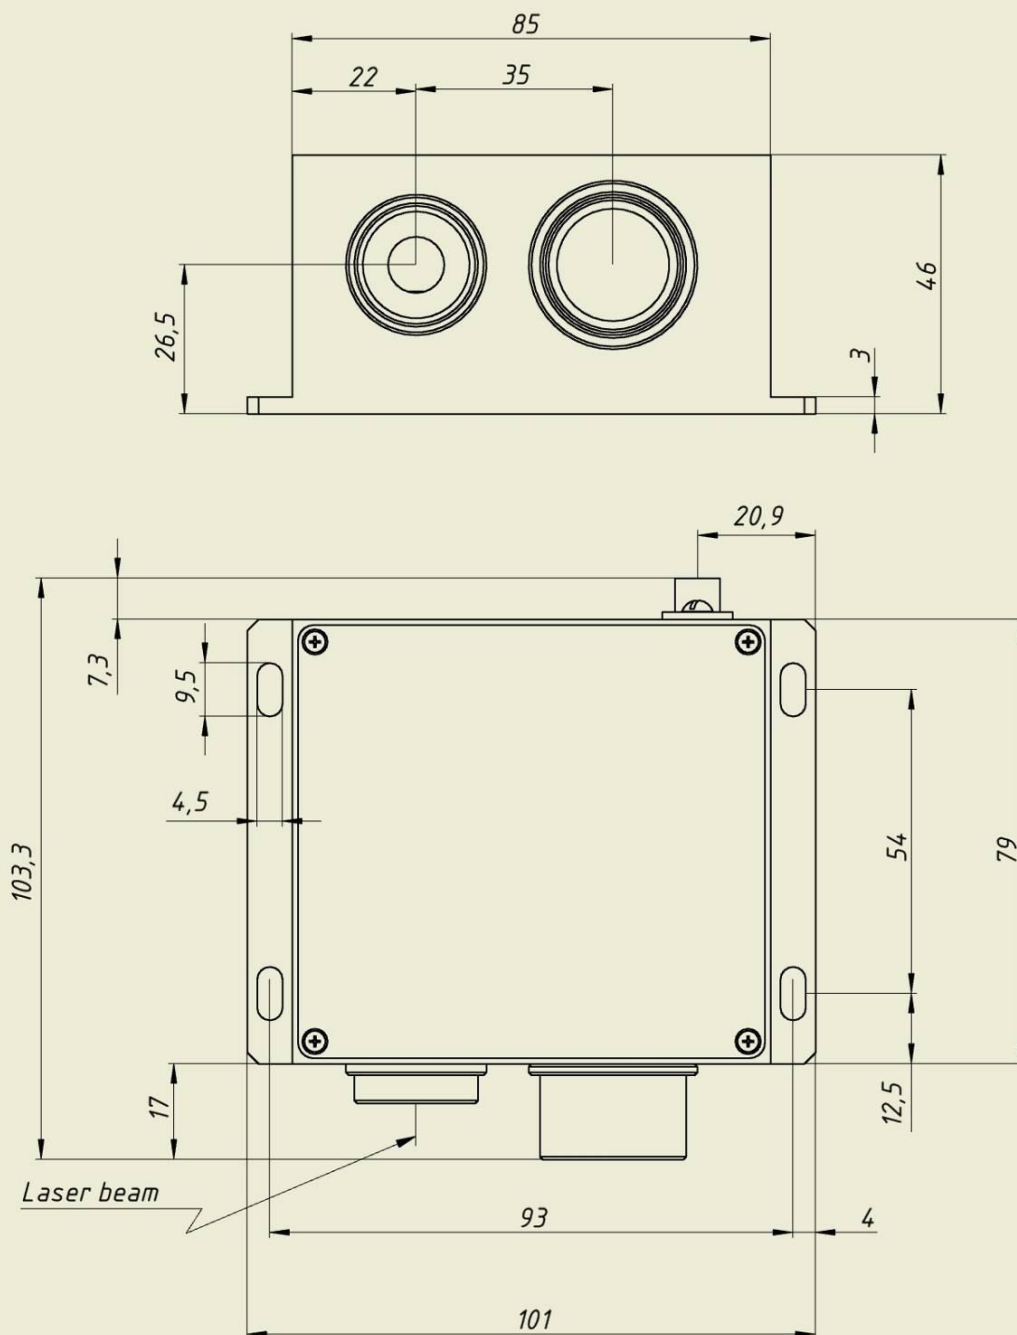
Габаритные и установочные размеры датчика ИСД-5
